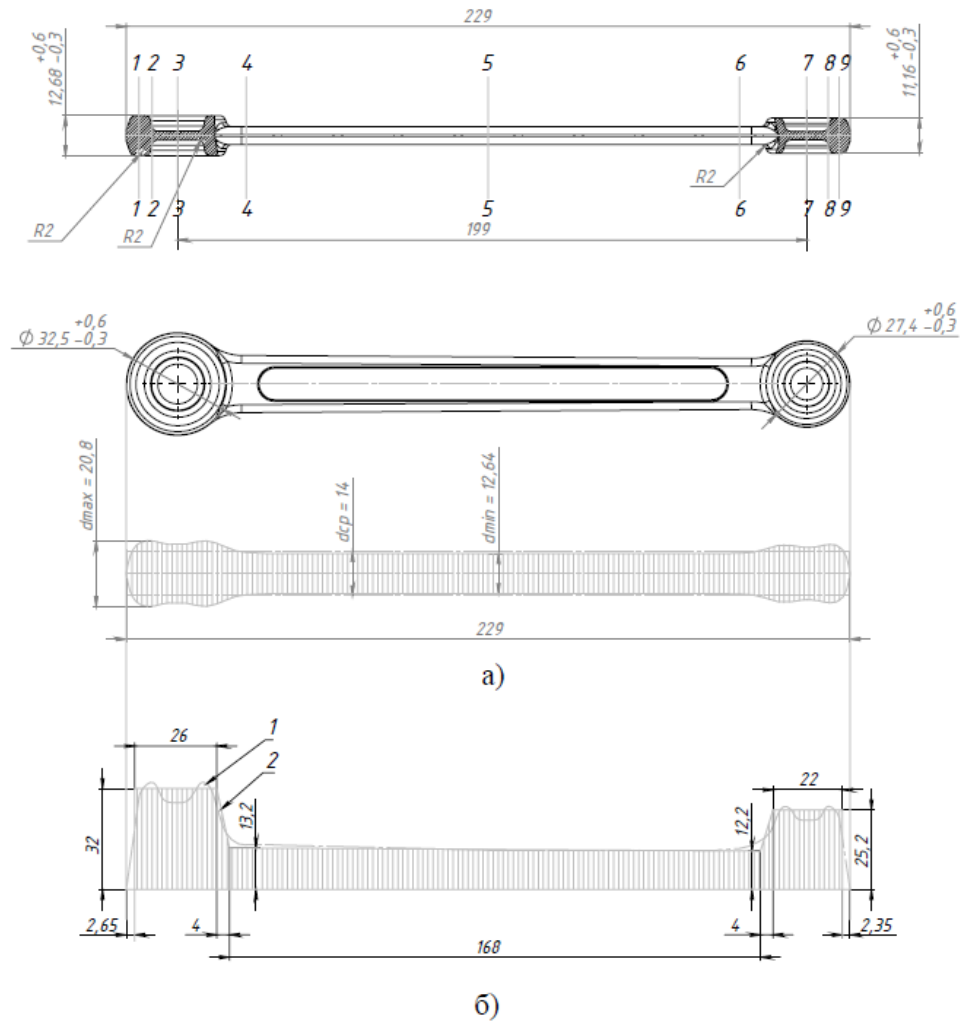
Эпюры диаметров и сечений: а – развертка поковки гаечного ключа и расчетная заготовка (эпюра диаметров); б – эпюры поперечных сечений (1 – поковки, 2 – вальцованной заготовки)
